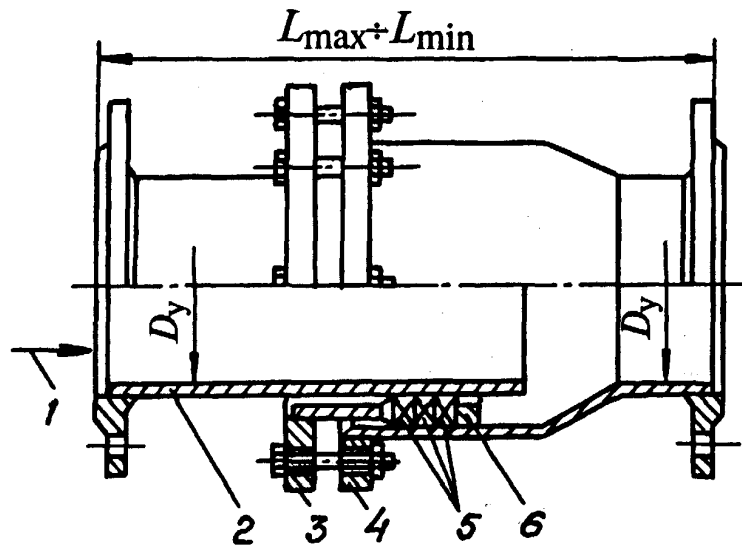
Компенсатор сварной сальникового типа:
